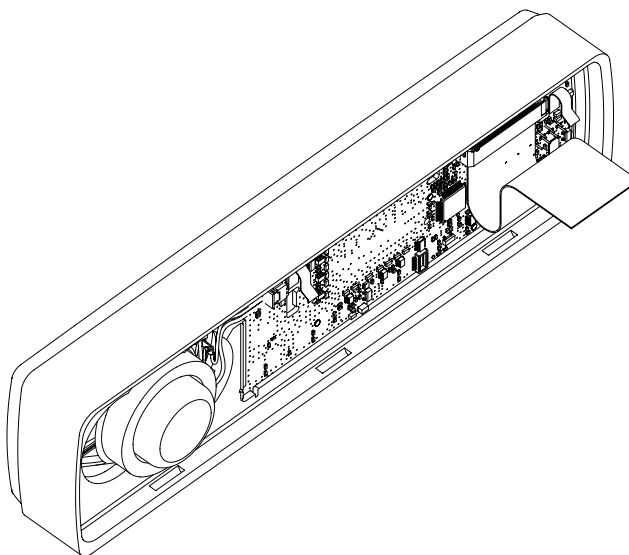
Montagem do Cabo Flexível da Cabeça de Controle à Placa da Cabeça de Controle
